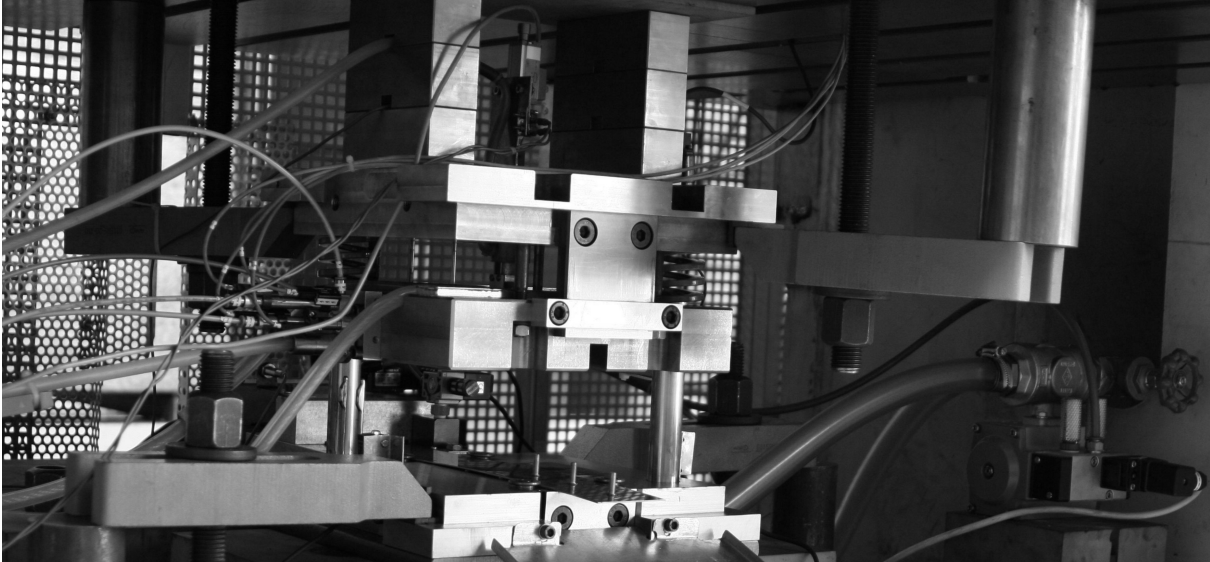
In der Presse eingerichtetes Versuchswerkzeug
